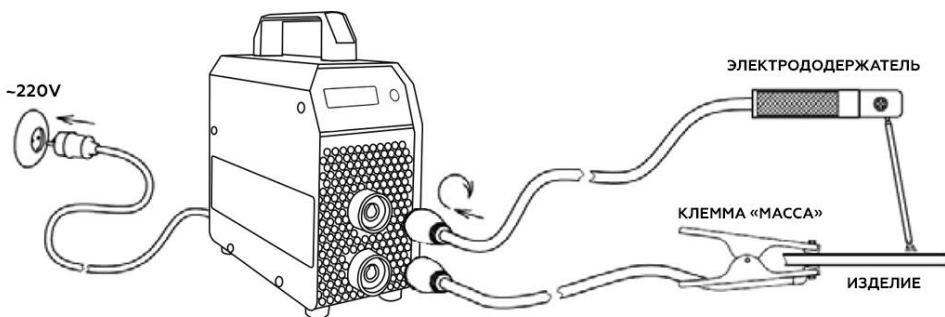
Схема подключения аппарата для сварки штучными электродами
